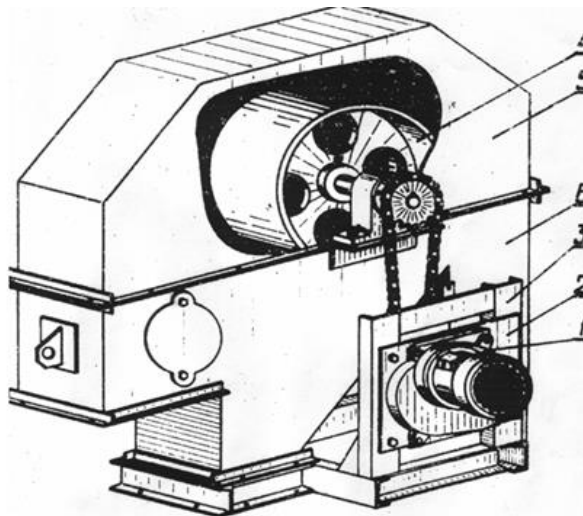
Головка норії: 1–привод; 2–піддвигунна плита; 3–рама; 4–барабан ведучий; 5–кришка; 6–корпус.
